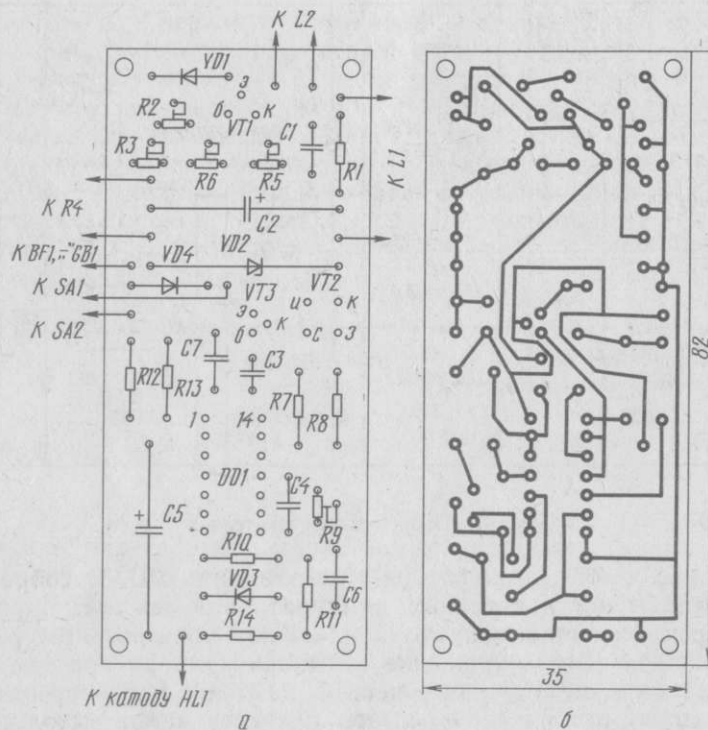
Печатная плата: а — вид со стороны деталей; б — вид со стороны печати
